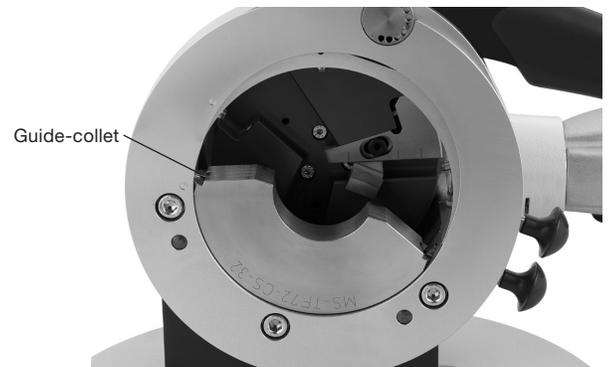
Installation du demi-collet inférieur (gros plan)
